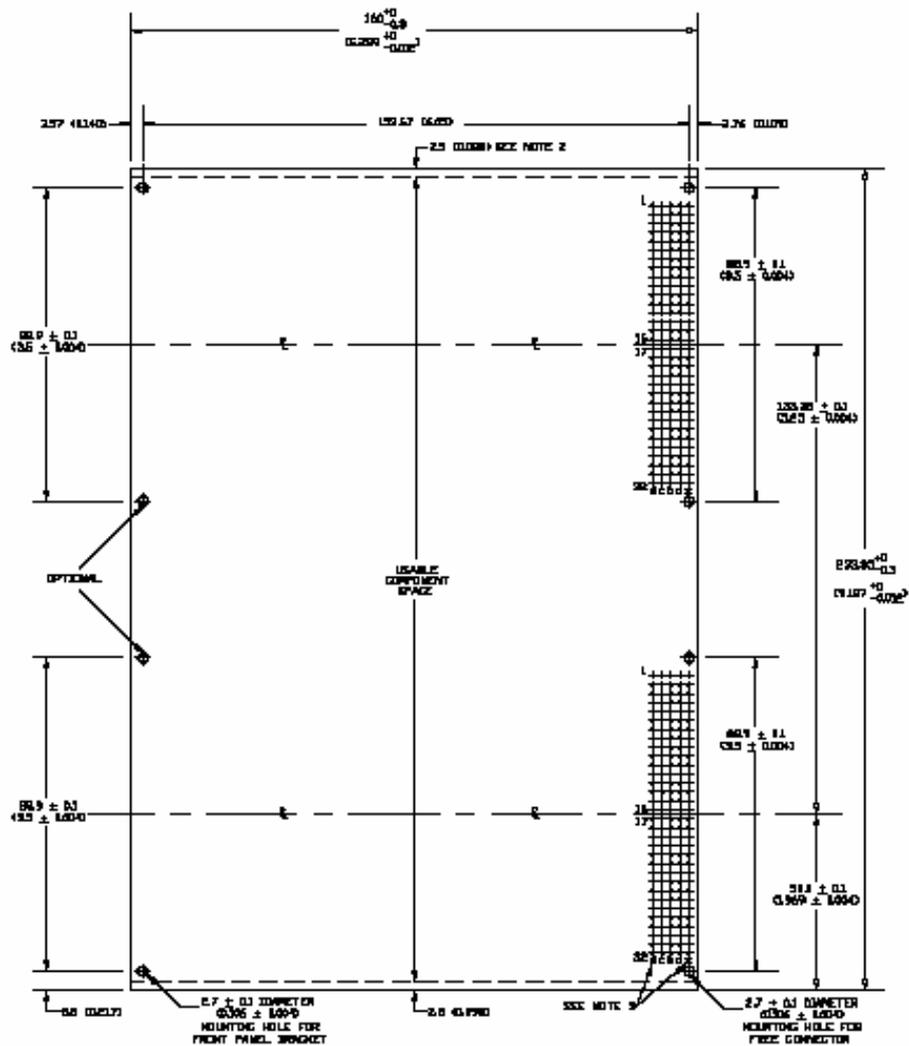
Dimensiones de la Optical Multiplexer Board.
